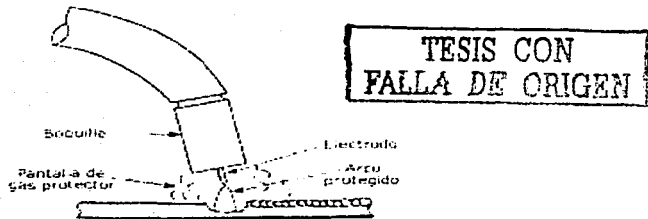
Esquema de un sistema de soldadura bajo gas protector [1].
